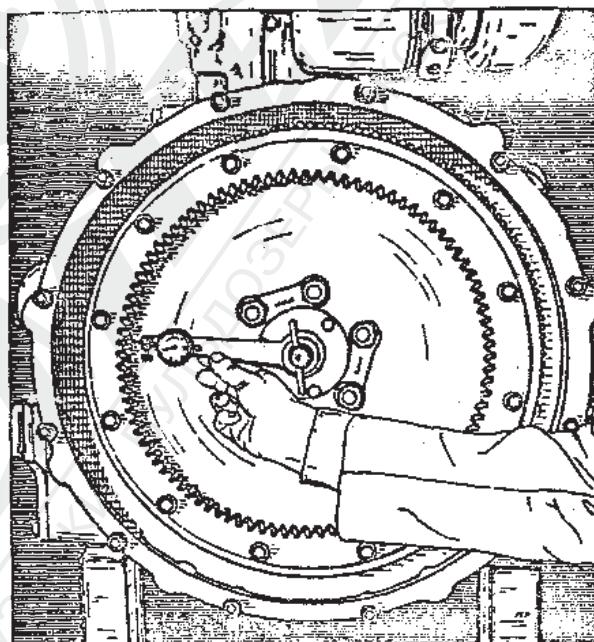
Контроль биения внутренних зубьев зубчатого кольца маховика двигателя
